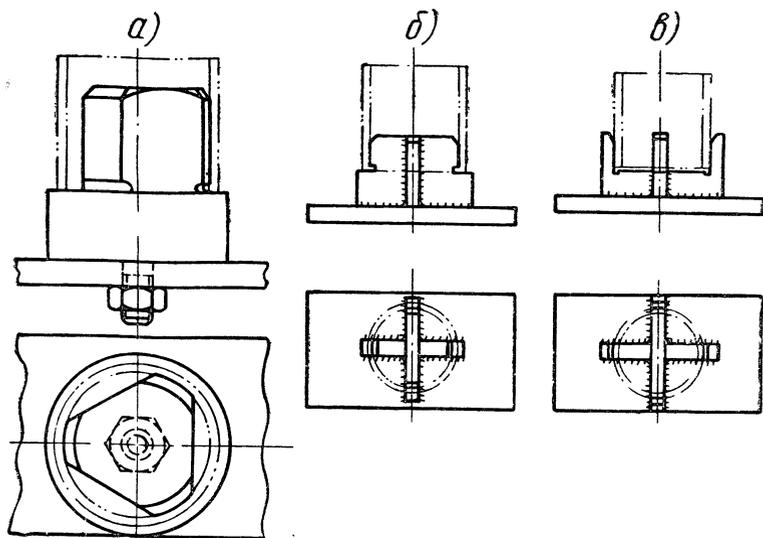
Установка длинной цилиндрической детали с помощью двух штырей.
